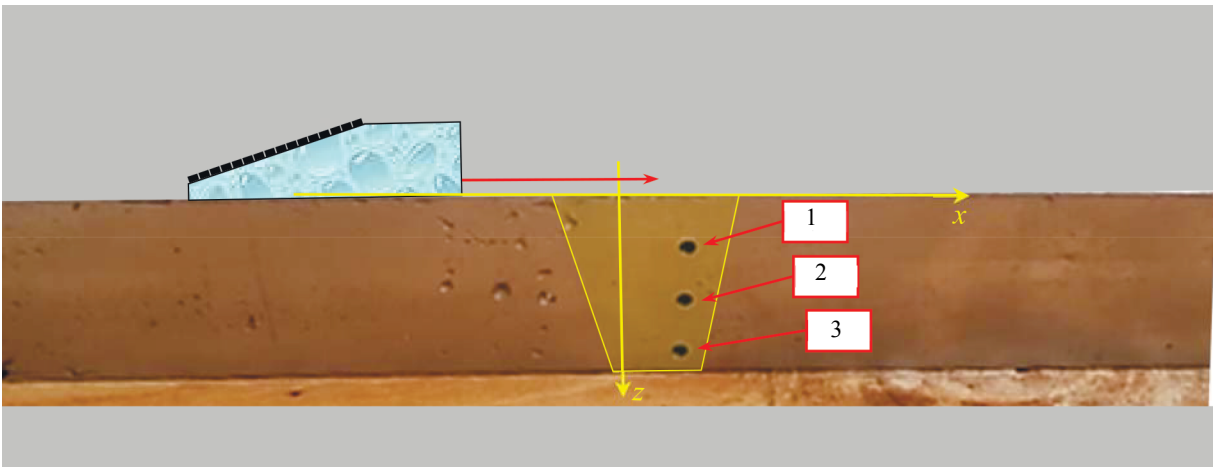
Образец с аустенитным V-образным сварным соединением.
